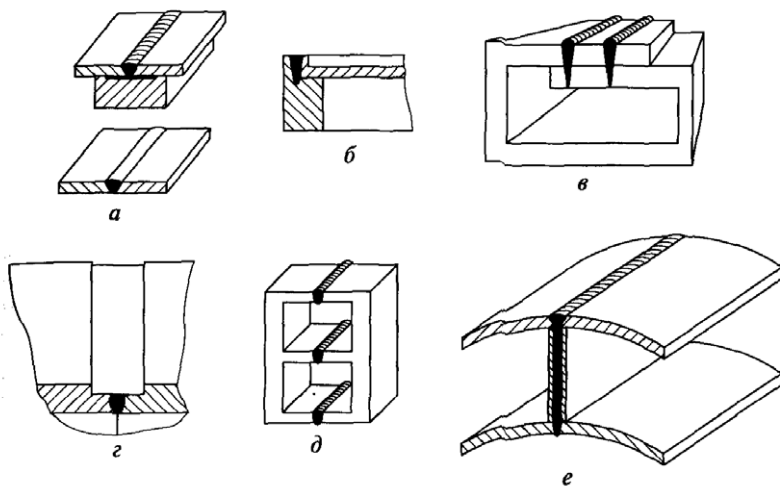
Основные типы соединений деталей при электронно-лучевой сварке: *a* – в стык тонколистовых деталей на подкладке и без нее; *б* – с отбортовкой кромок различной толщины; *в* – внахлестку; *г* – в узких разделках и труднодоступных местах; *д* – однопроходная сварка одновременно нескольких стыков проникающим лучом; *е* – сварка двух цилиндров электронным лучом через ребро жесткости
